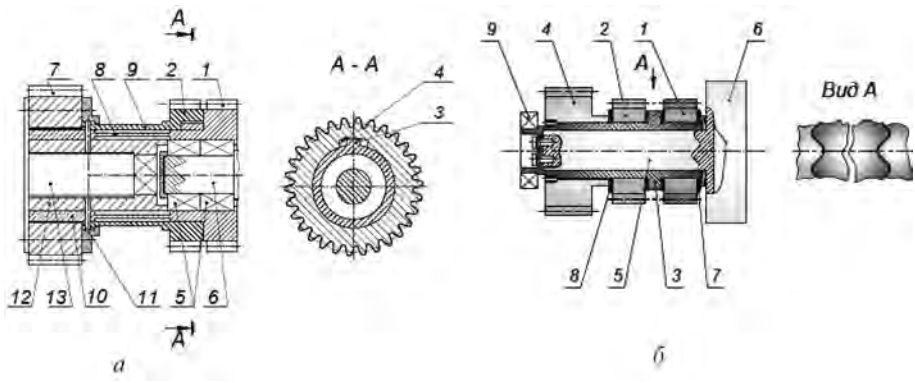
Схемы узла сателлита с упругой связью между его зубчатыми венцами: *a* – торсионного типа [13, 19]: 1, 2 – зубчатые венцы сателлита, 3 – упор, 4 – ограничительный паз, 5 – подшипники качения, 6 – кривошип водила, 7 – дополнительный зубчатый венец, 8, 9 – трубчатые торсионы, 10, 11 – опоры торсионов, 12 – фиксирующая втулка, 13 – дополнительный торсион; *б* – осевого типа: 1, 2 – зубчатые венцы сателлита, 3 – втулка с «мышинным зубом» на торцах фланца, 4 – дополнительный зубчатый венец, 5 – кривошип, 6 – направляющие радиальных перемещений сателлита, 7, 8 – тарельчатые пружины
